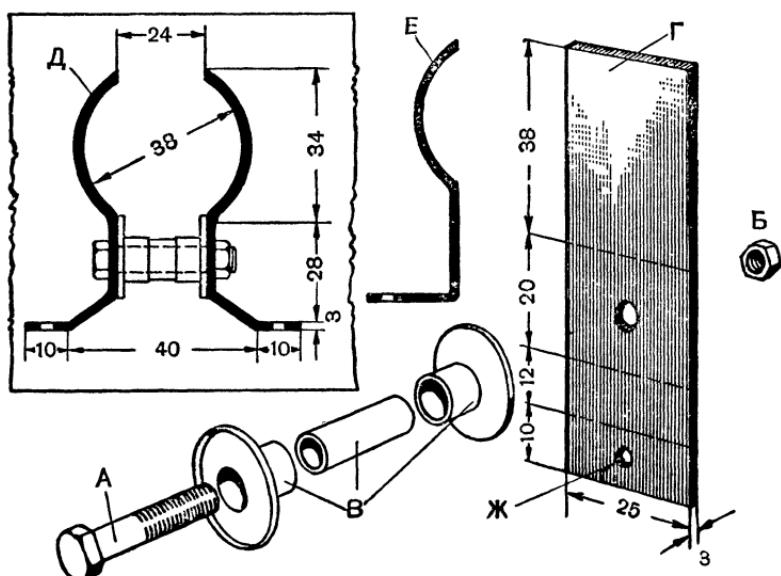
Детали статора № 1 (рис. 10): А — болт; Б — гайка; В — части каркаса катушки; Г — заготовка для башмака; Д — башмаки изогните вот так; Е — так тоже можно изогнуть башмаки; Ж — это отверстие сверлите, когда изогнете башмак.
